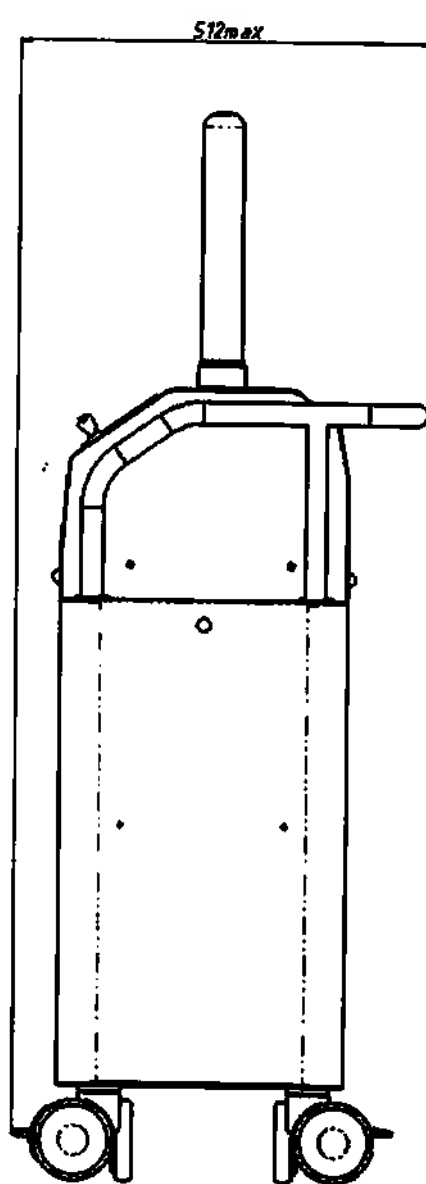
Габаритные размеры Изделия в транспортировочном положении
